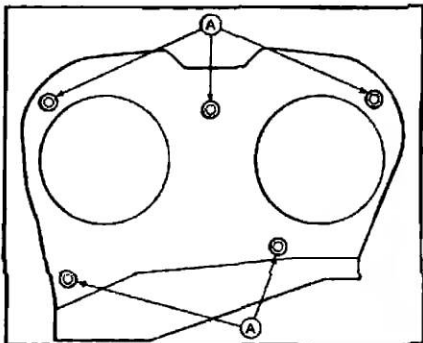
Расположение болтов крепления верхнего кожуха зубчатого ремня
